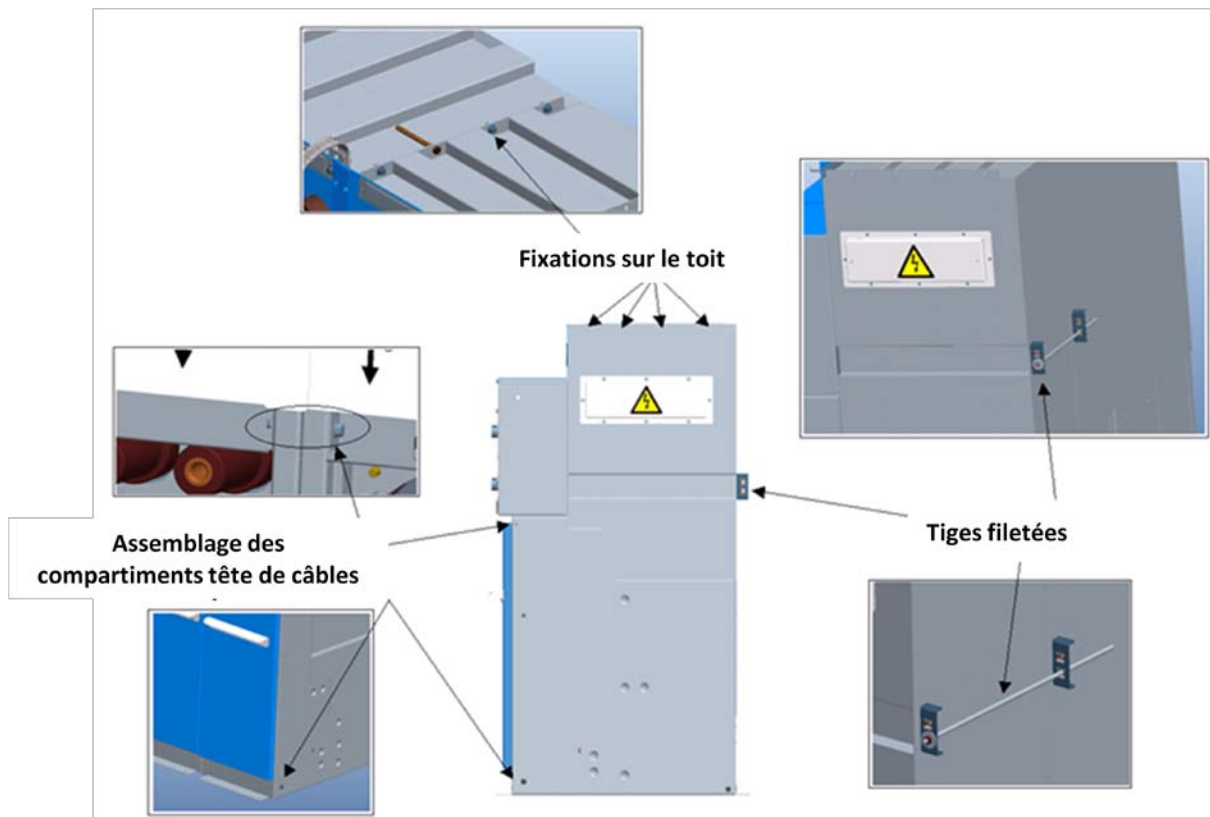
Vue d'ensemble des points de liaison des RMU'S
